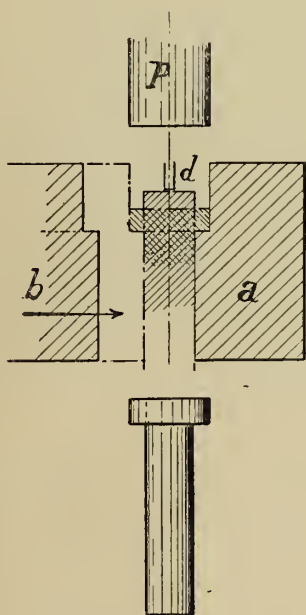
Schéma du fonctionnement des machines à refouler.
